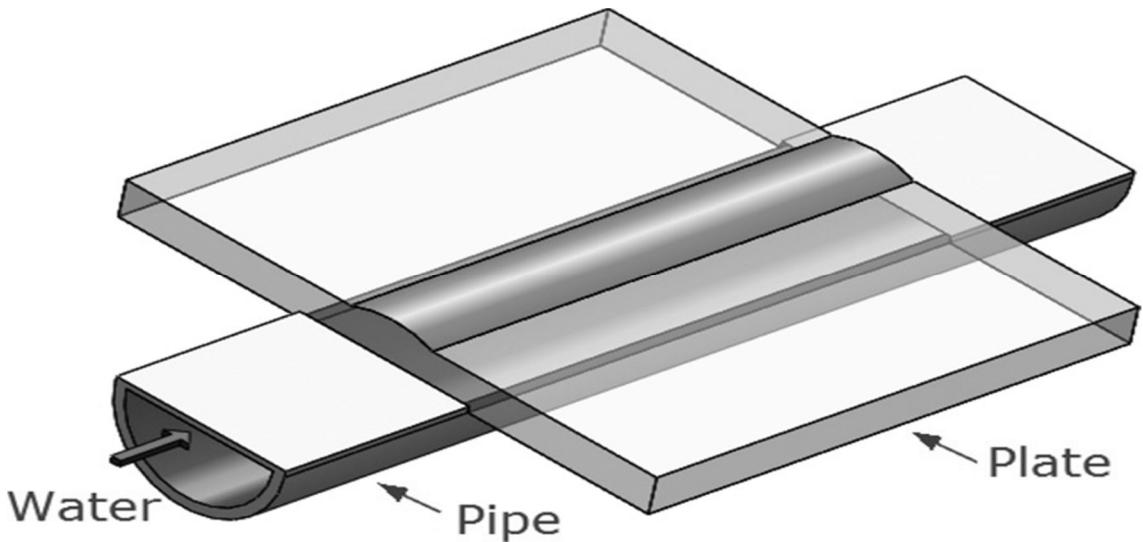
냉각 파이프를 이용한 heat sink welding(HSW) 모식도
